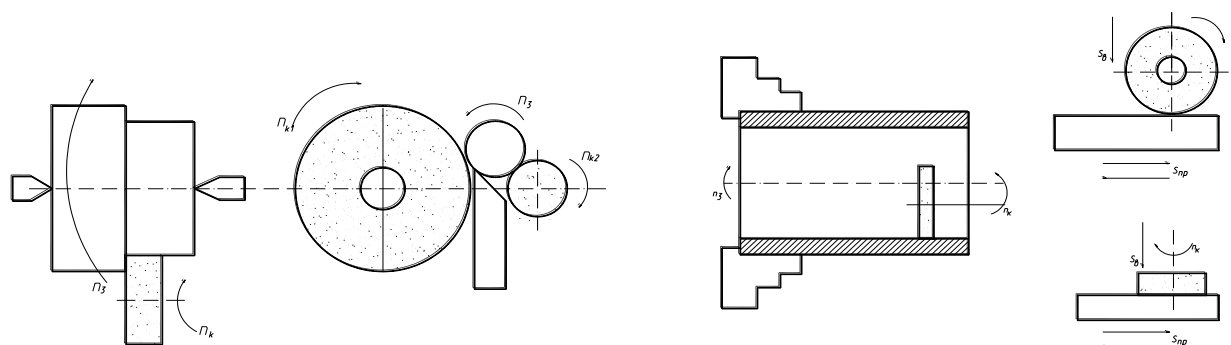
Схема обработки заготовок на шлифовальных станках
